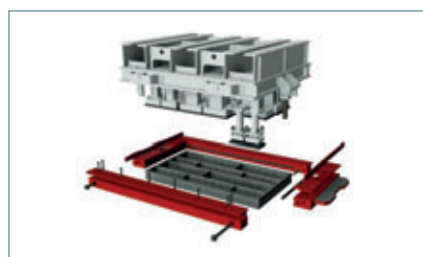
Sistema modular de moldes de Kobra con centrado forzado «Headguide™»
